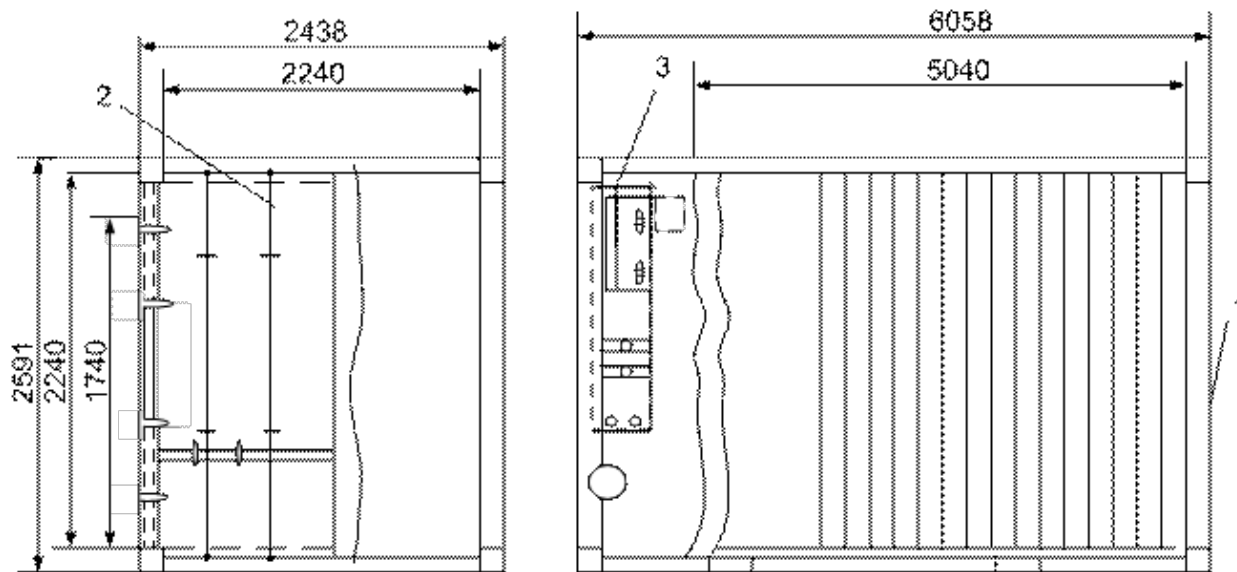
Зовнішній вигляд РК типу 1СС із габаритними розмірами де: 1 – корпус контейнера; 2 – двері притуленого типу; 3 – рефрижераторний агрегат
